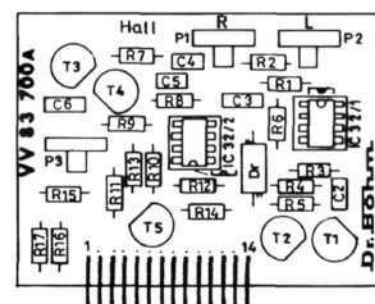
Positionsnummernplan Hall-Modul Platine VV 83 700 A
